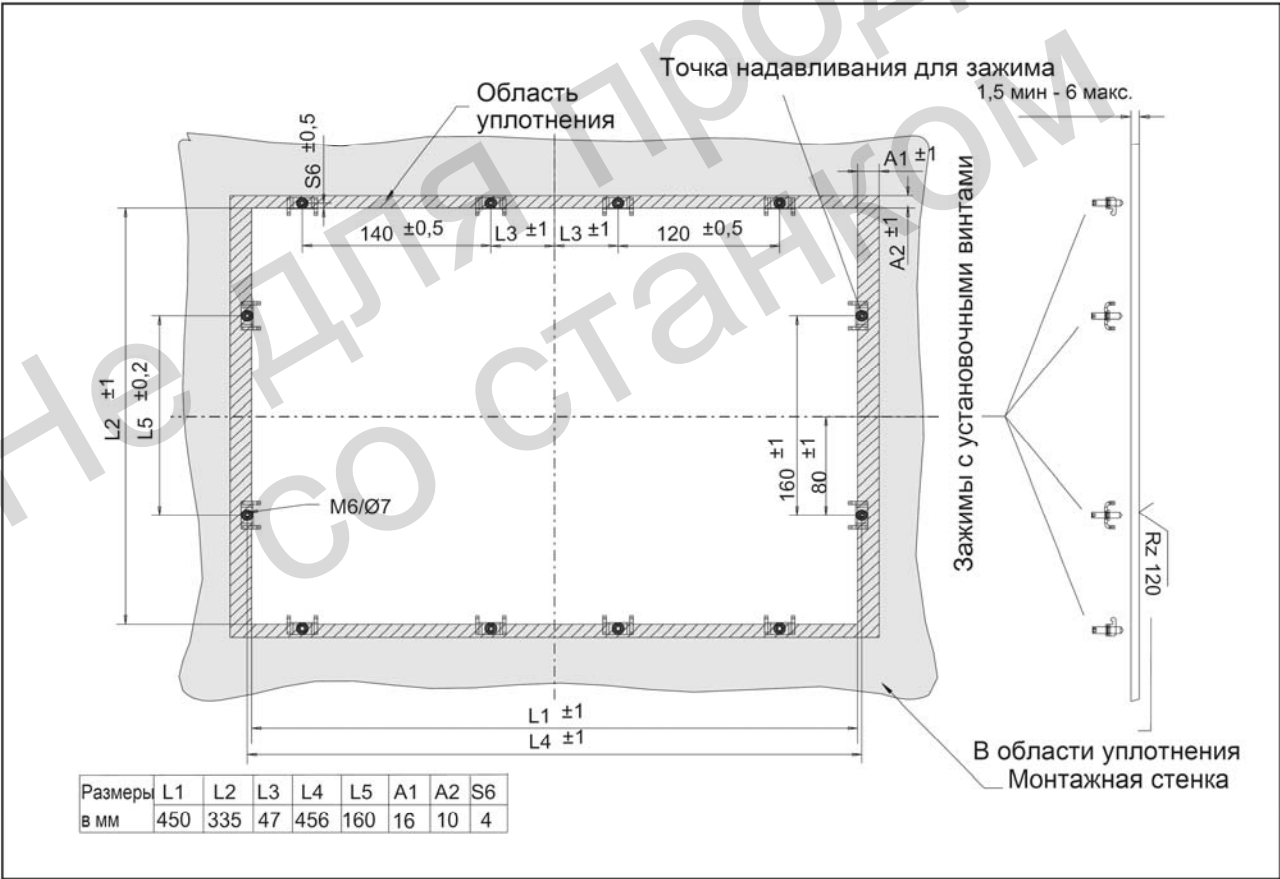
Габаритный чертеж для монтажа панели оператора OP 015A
